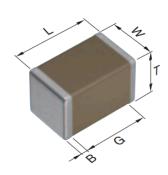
Габаритный чертеж корпуса SMD чип-радиокомпонента и его конструктивные размеры.
